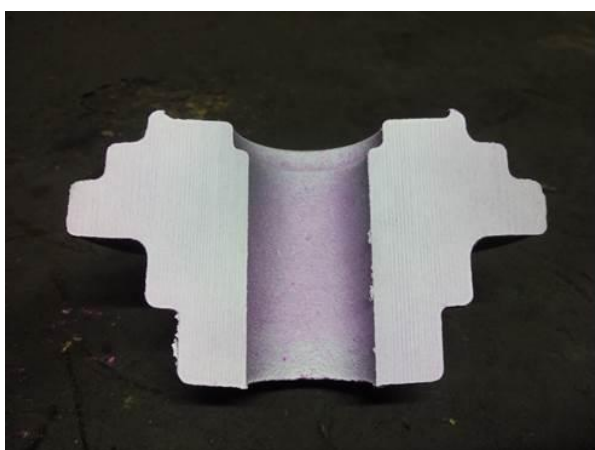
Foto da peça 5, cortada segundo o plano de separação, depois do ensaio de Líquidos Penetrantes.
